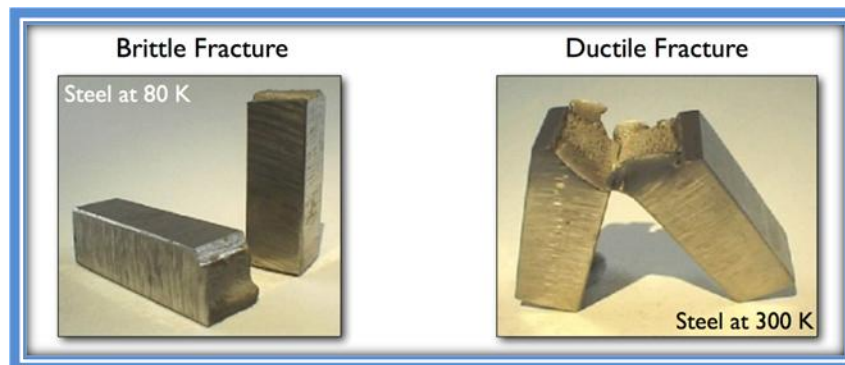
Tipos de fractura Frágil - (Brittle fracture), - Dúctil (Ductile fracture)
